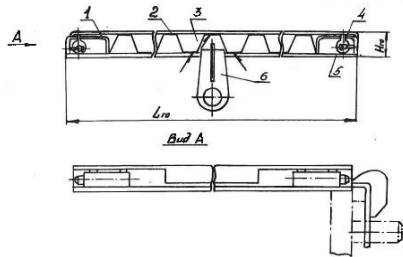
Гибкая оболочка: 1- направляющий паз; 2 – верхний лист; 3 – гофрированный наполнитель; 4 – направляющая; 5 – нижний лист; 6 - кронштейн
